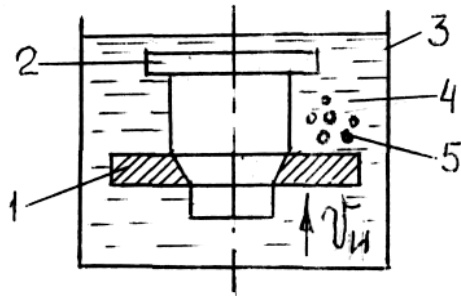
Схема зворотного копіювання: 1 – електрод-інструмент; 2 – заготовка; 3 – ванна; 4 – діелектрик; 5 – продукти обробки
